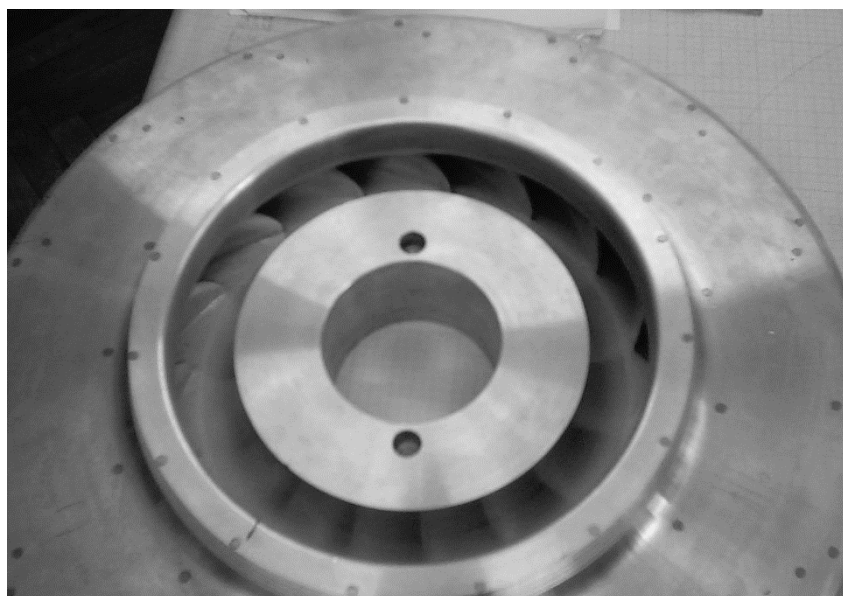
Закрытое рабочее колесо с цельнофрезерованными лопатками и приклепанным покрывающим диском (кафедра КВХТ СПбГПУ)
